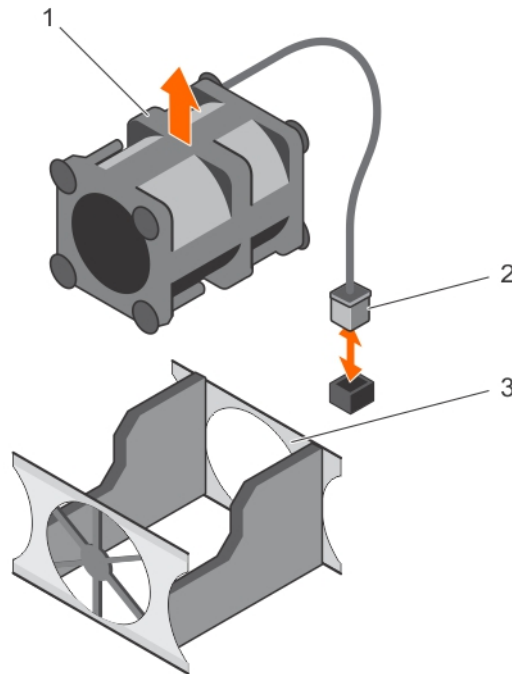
Retrait et installation d'un ventilateur de refroidissement
